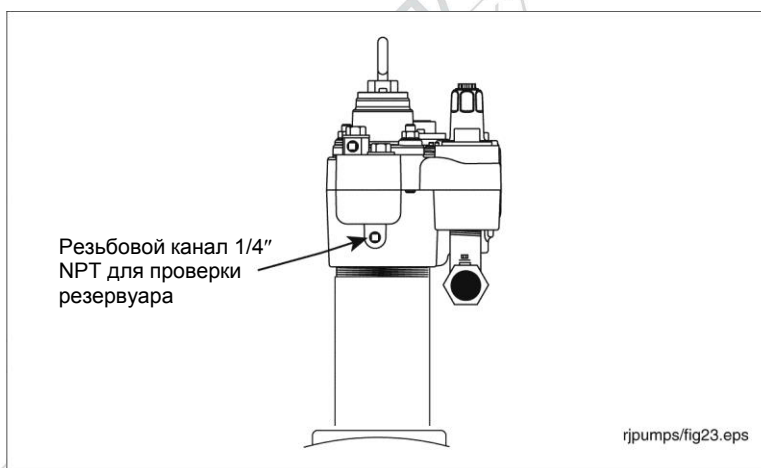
Находящийся на манифольде канал для проверки резервуара
